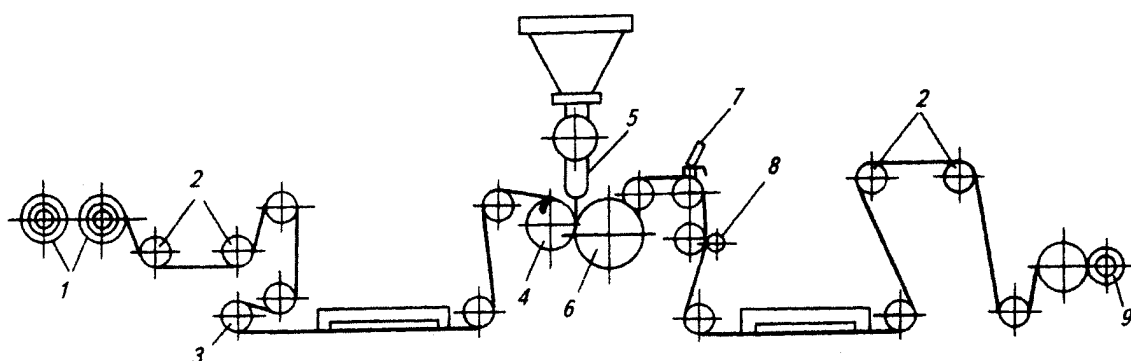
Схема экструзионно-ламинаторного агрегата: 1 – раскат; 2 – бумаговедущий валик; 3 – натяжной валик; 4 – прижимной вал; 5 – экструдер; 6 – хромированный холодильный цилиндр; 7 – устройство для ионизации; 8 – ножи; 9 – накат
